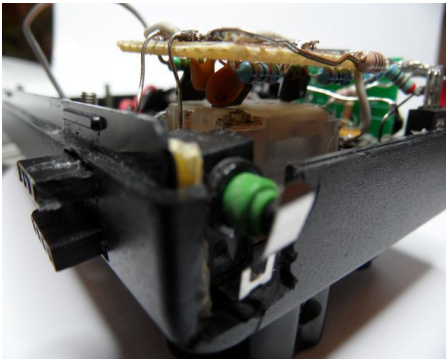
die Baugruppe wurde beim Einbau zu hoch.
